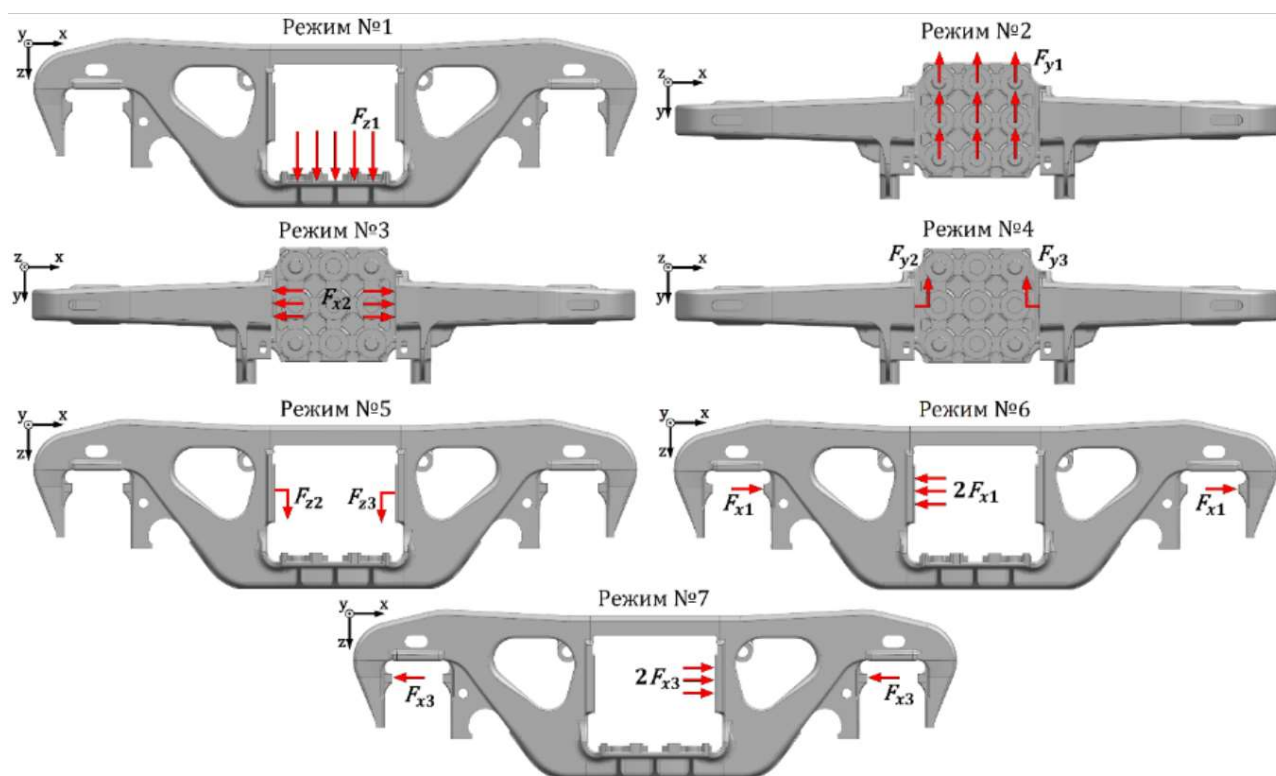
Розрахункові режими для бічної рами [82]
